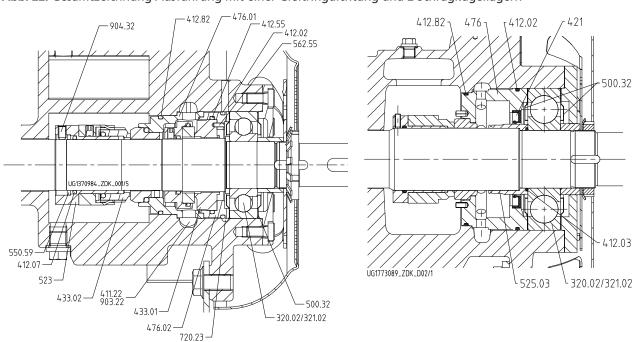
Gesamtzeichnung Ausführung mit einer Gleitringdichtung und 2 Schrägkugellagern
